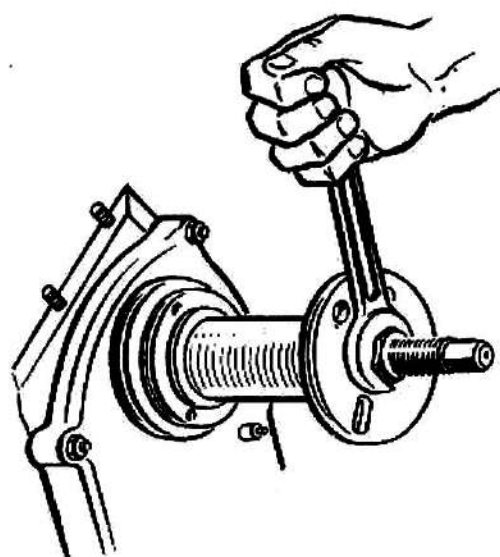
Напрессовка ступицы шкива коленчатого вала с помощью приспособления 16-У-236817
